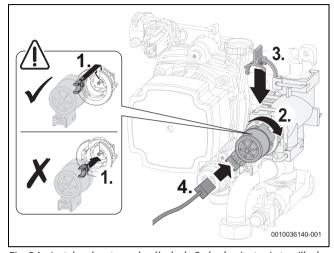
Instalar el motor en la válvula de 3 vías (variante sin tornillos)
